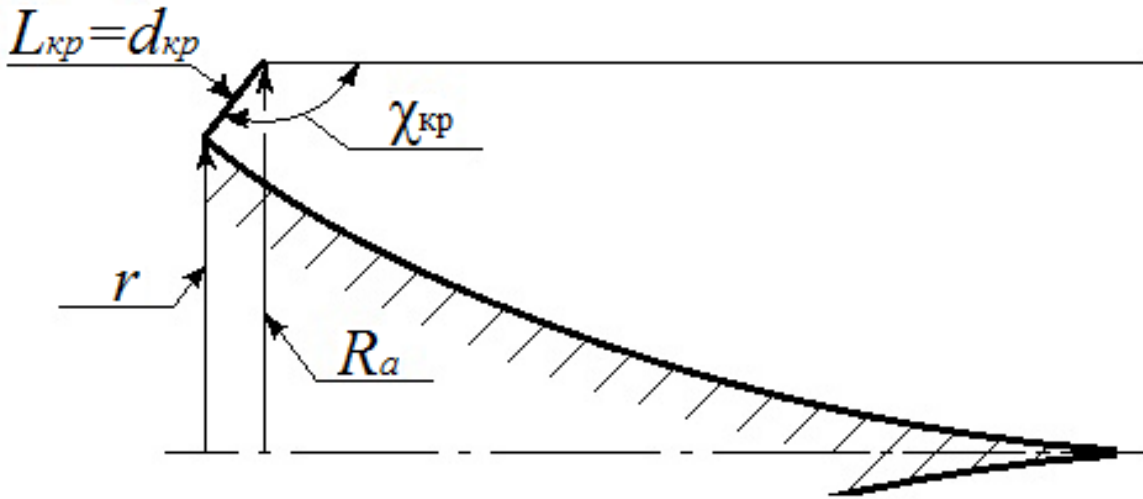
Расчетная схема к определению коэффициента перекрытия
